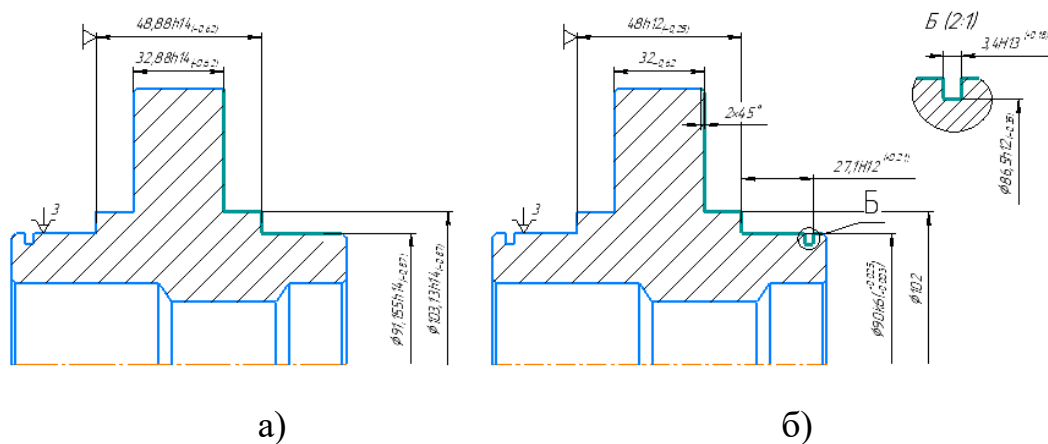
Заготовка после токарной обработки а) черновой, б) чистовой
